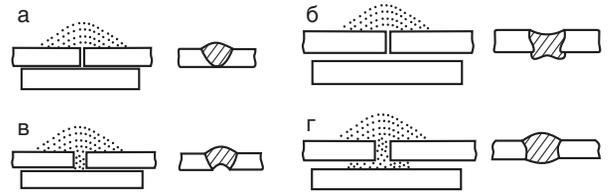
Схема односторонней автоматической сварки стыковых соединений на медной подкладке
